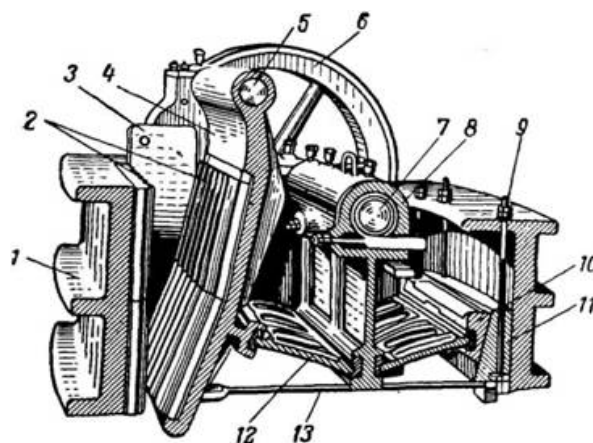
Устройство щековой дробилки типа ЩДП¹
